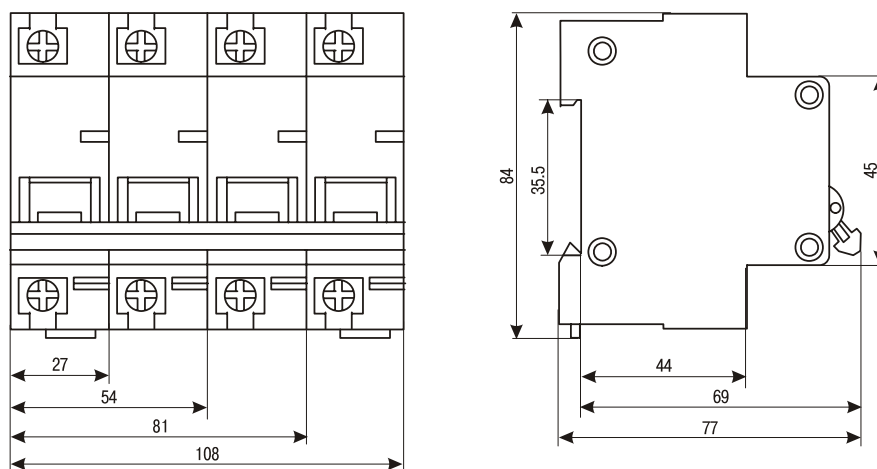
Габаритные и установочные размеры ВА47-100
